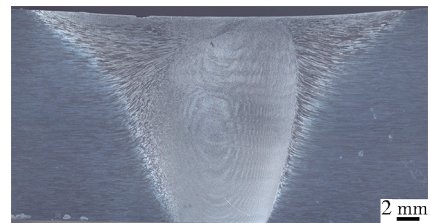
为20 mm厚2219C10S铝合金在不同搅拌头旋转速度下的搅拌摩擦焊接接头宏观组织形貌。从总体上看,焊接接头的宏观组织形貌非常相似,均由轴肩影响区(SAZ)、焊核区(WNZ)、前进侧/后退侧热力影响区(TMAZ-A/R)、前进侧/后退侧热影响区(HAZ-A/R)和母材区(BM)等组成,各个区域的位置如图3(a)所示。其中,前进侧热力影响区与焊核区的分界线几乎为一条直线,呈倒三角状,越接近焊缝上表面的热力影响区越宽,在靠近下表面的1/3厚度范围内热力影响区的范围很小,晶粒的拉长和扭曲变形相对很小;后退侧热力影响区呈楔形,进入焊缝内部约至焊核区宽度的1/2,其上部为轴肩影响区,下部为焊核区。轴肩影响区靠近焊缝上表面,后退侧轴肩影响区的范围明显大于前进侧,且随着搅拌头旋转速度的增大而增大。热力影响区和轴肩影响区的组织在前进侧与后退侧的差异,是由母材在焊接过程中受到不同的搅拌作用力、从而导致金属的塑性流动模式的差异造成的。在前进侧,母材金属组织主要受到搅拌针的剪切作用,因此塑性流动的方向矢量沿厚度方向的分量较大;而后退侧金属的
